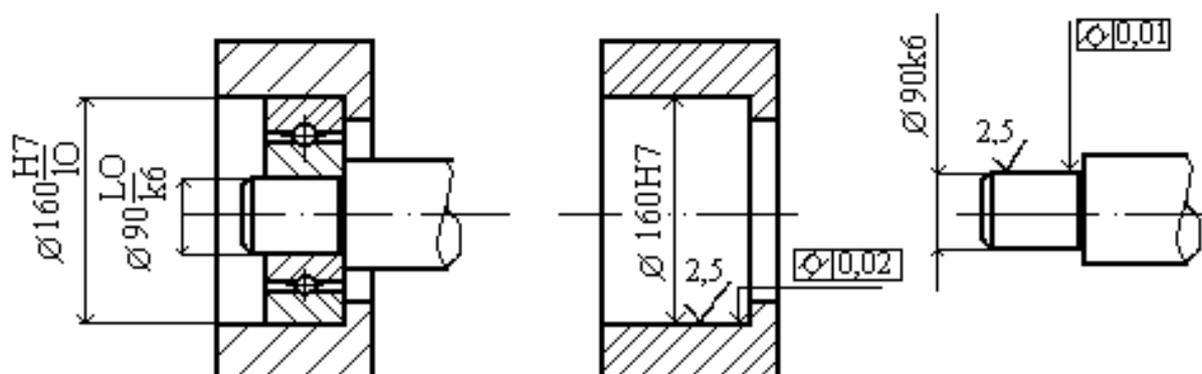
Обозначение допусков и посадок подшипников качения
